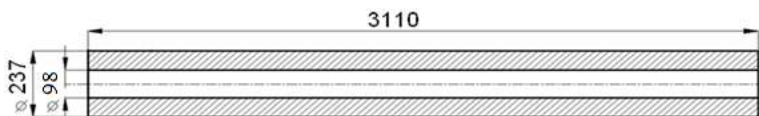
Заготовка для полых вагонной оси типа РУШ
